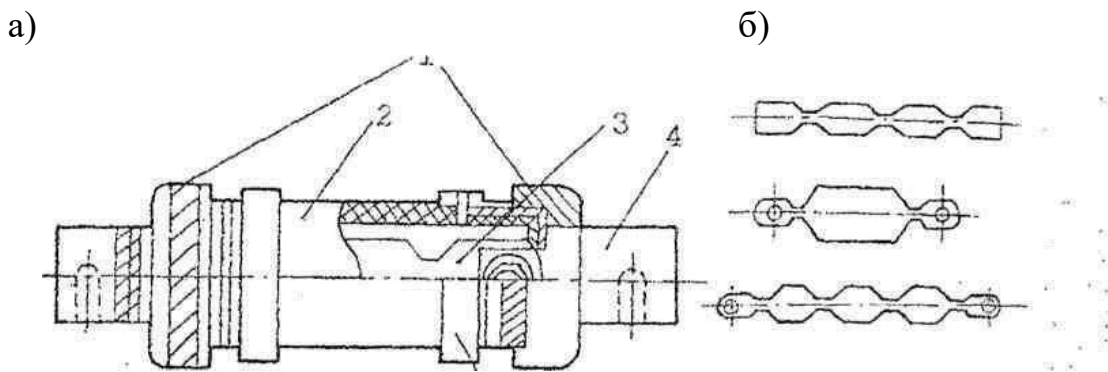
Предохранитель типа ПР-2: а) конструкция предохранителя: 1 - контактные держатели, 2 - фибровая трубка, 3 - плавкая вставка, 4 - контактный нож, 5 - медная шайба; б) форма плавких вставок
